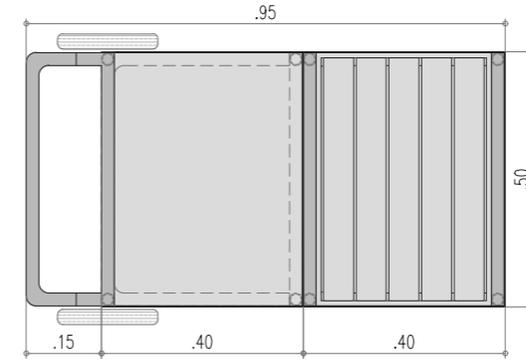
Planta puesto de venta ambulante tipo 4. Esc 1:15
